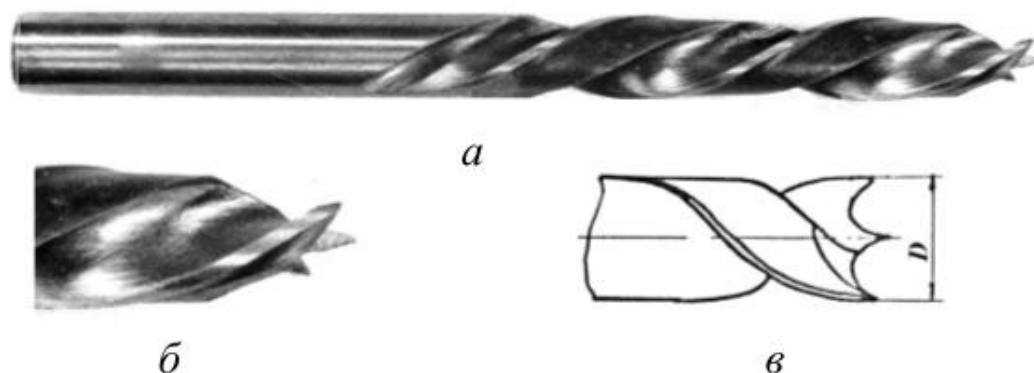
Сверло с центром и периферийными подрезателями:
